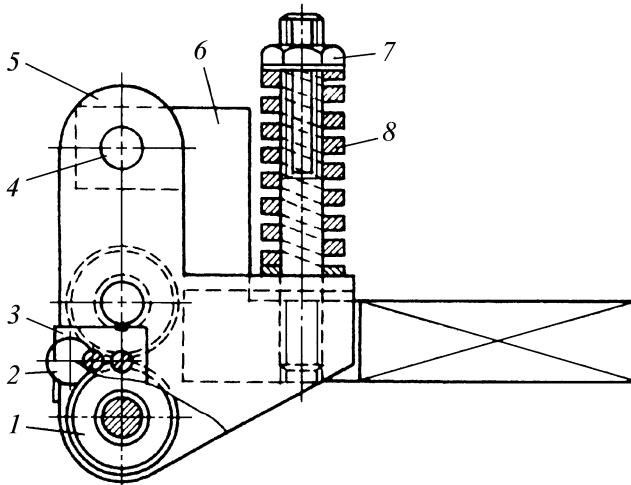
Одношариковый обкатник рычажного типа для обработки открытых поверхностей закаленных деталей:
